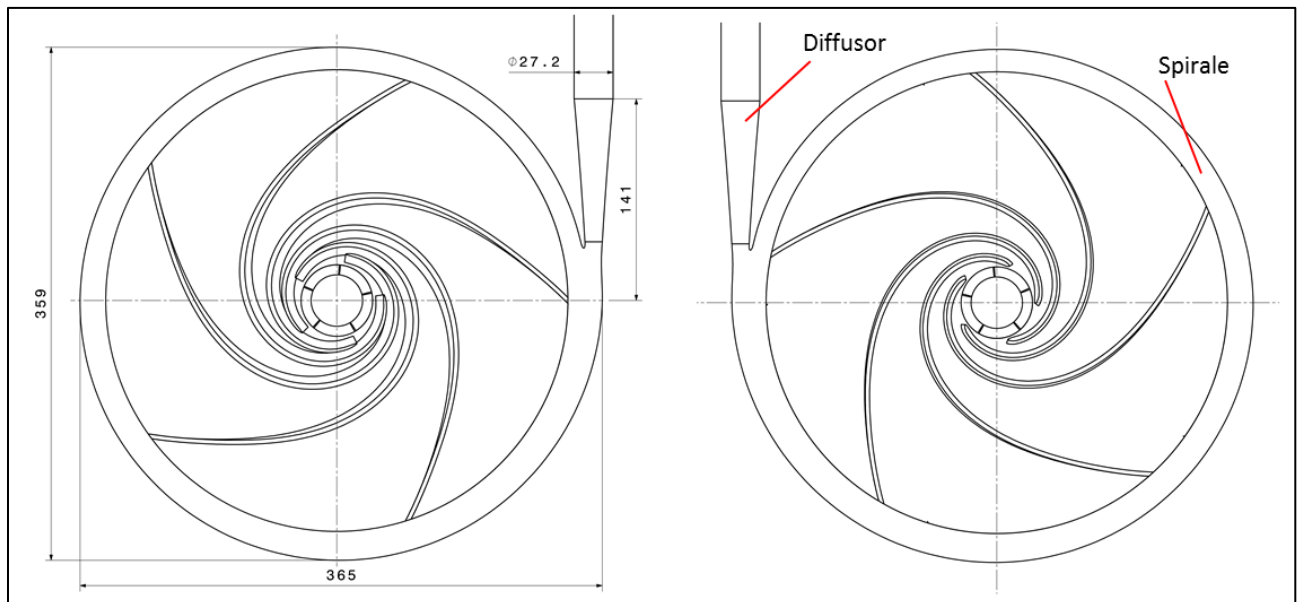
Draufsicht (links) und Rückansicht (rechts) der Pumpe für die mechanische Fertigung mit  $n_q = 4 \text{ min}^{-1}$
